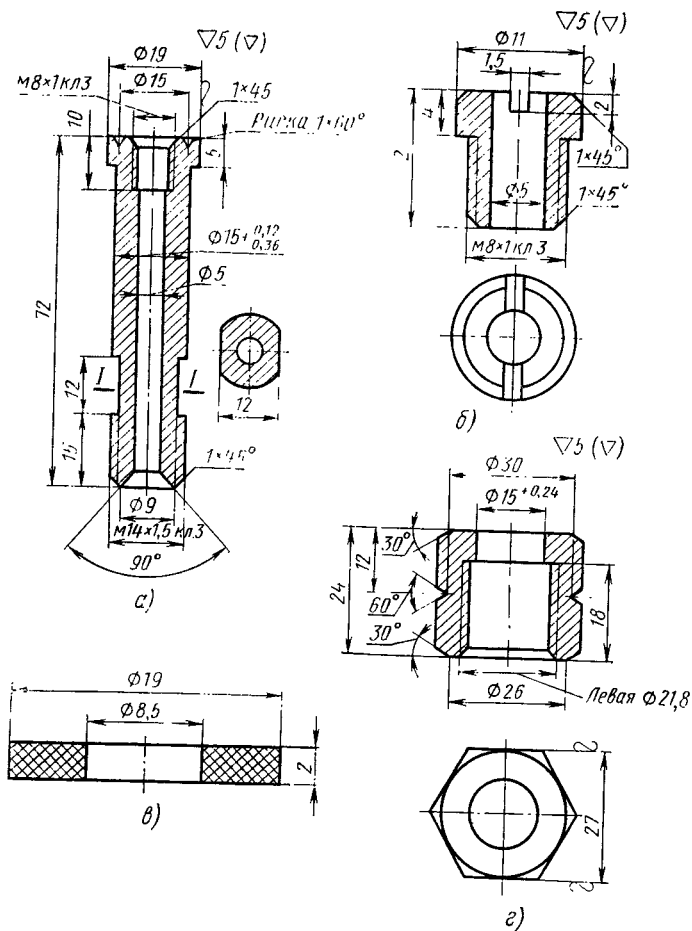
Детали для переделки ацетиленового редуктора на пропановый:
